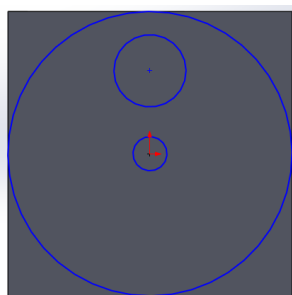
Marcado corte Imagen 68: Corte por laser Imagen 69: Pieza cortada
